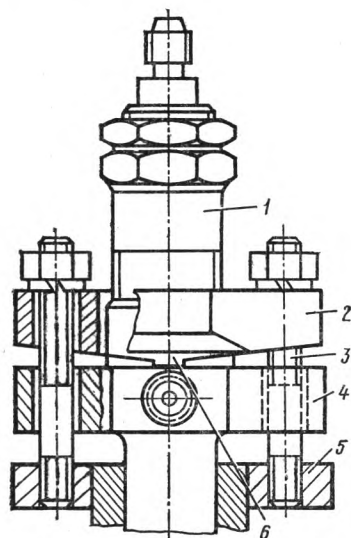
Крепление форсунки дизеля Д100 с помощью нажимного фланца: 1 — стакан пружины; 2 — нажимной фланец; 3 — шпилька; 4 — корпус форсунки; 5 — адаптер; 6 — опорная поверхность
